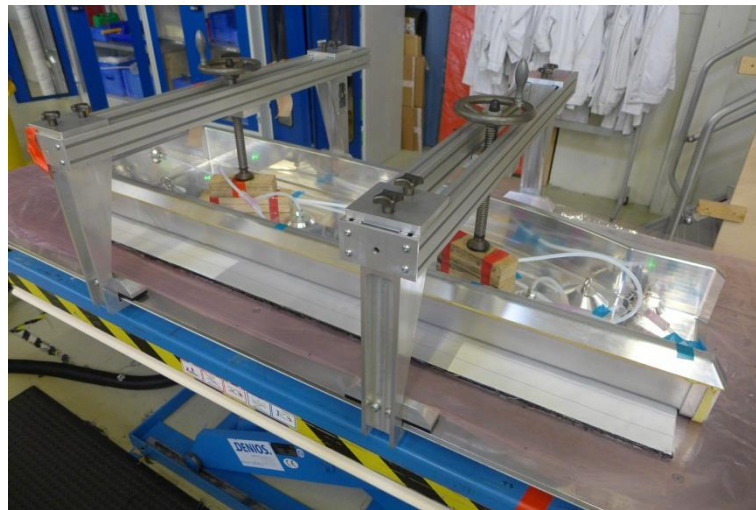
Fixierung des Werkzeugs auf der Preform
